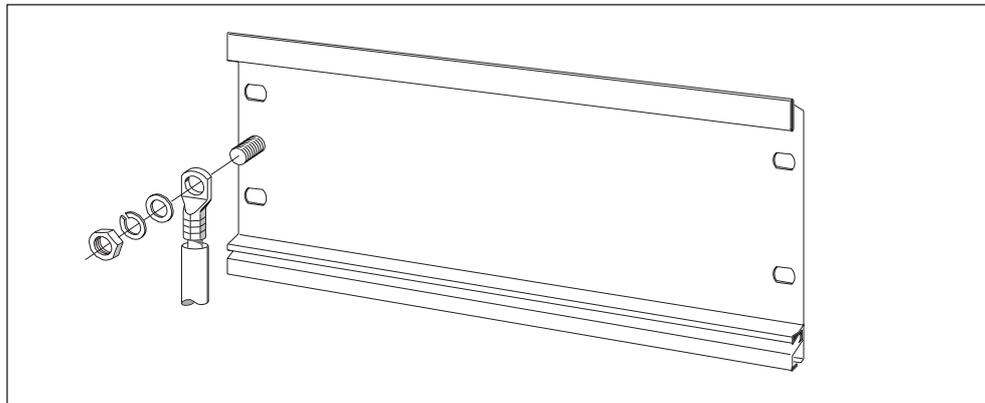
Raccordement du conducteur de protection sur le profilé-support
